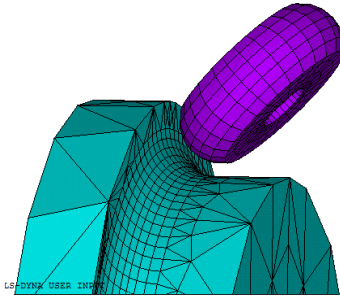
Динамическая модель обкатки роликами коленчатого вала
